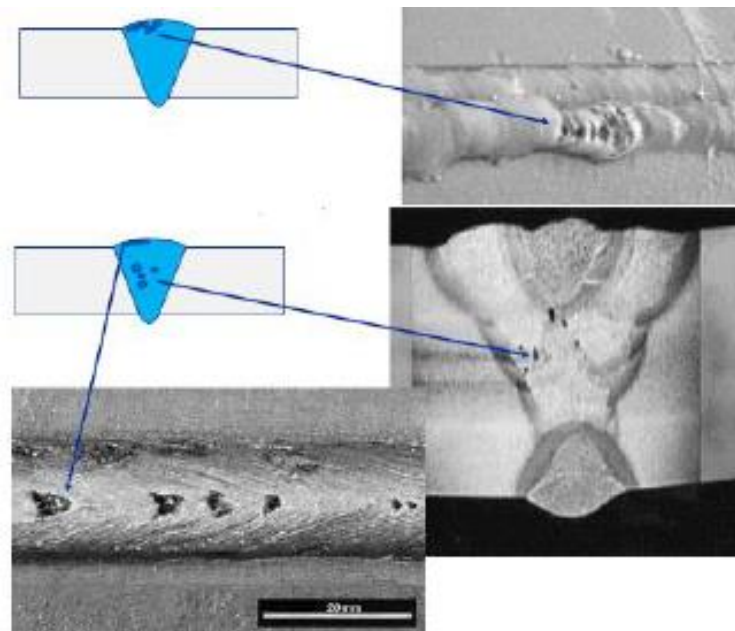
Exemplos de porosidades em juntas de soldadura [6]
